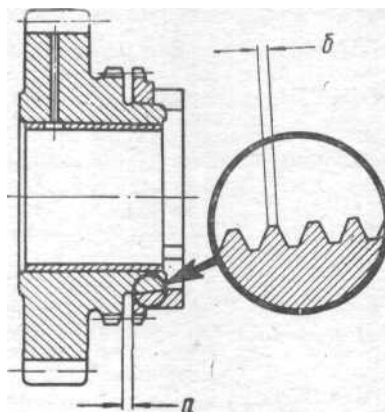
Установка блокирующего кольца синхронизатора на конусе шестерни
